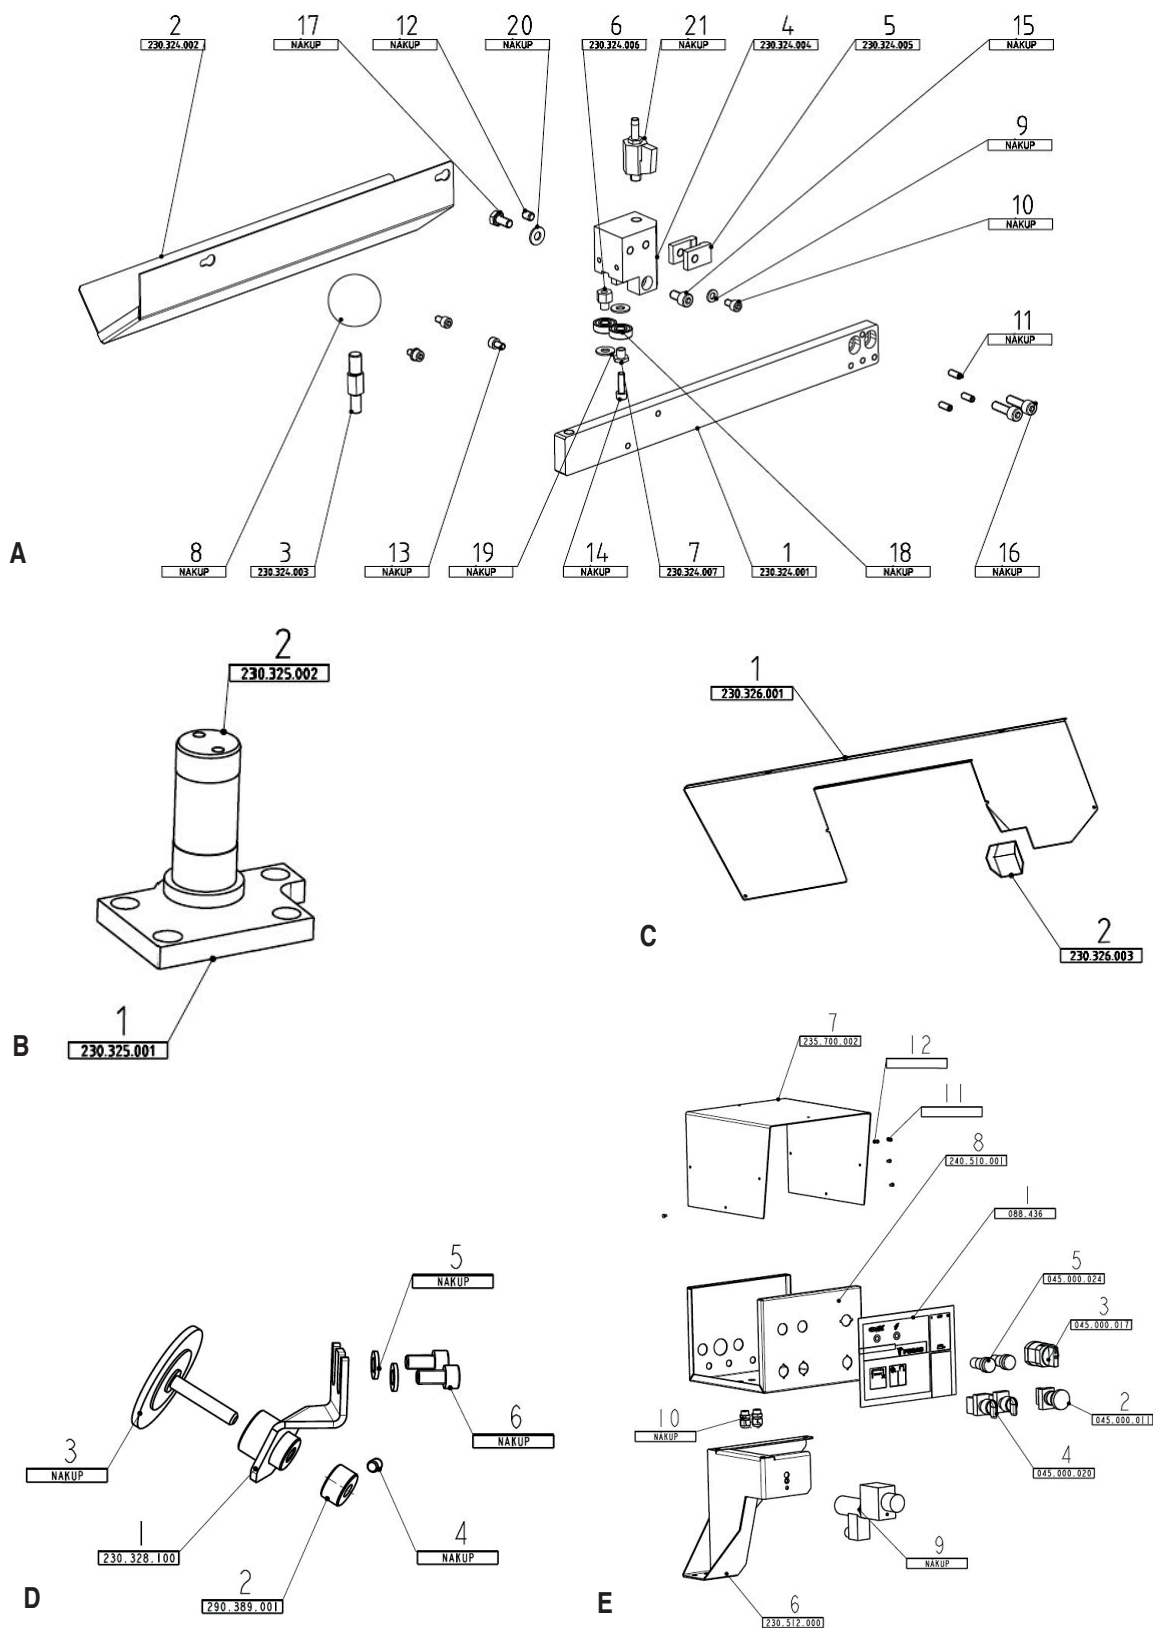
Dessin des pièces détachées 7 - A: Guide de lame mobile - B: Butée - C: Carter de protection des roues
